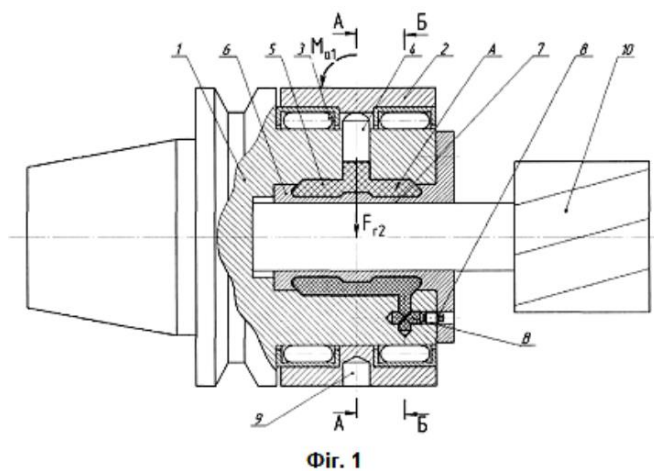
Затискний механізм з поворотною обоймою та підшипниками кочення
